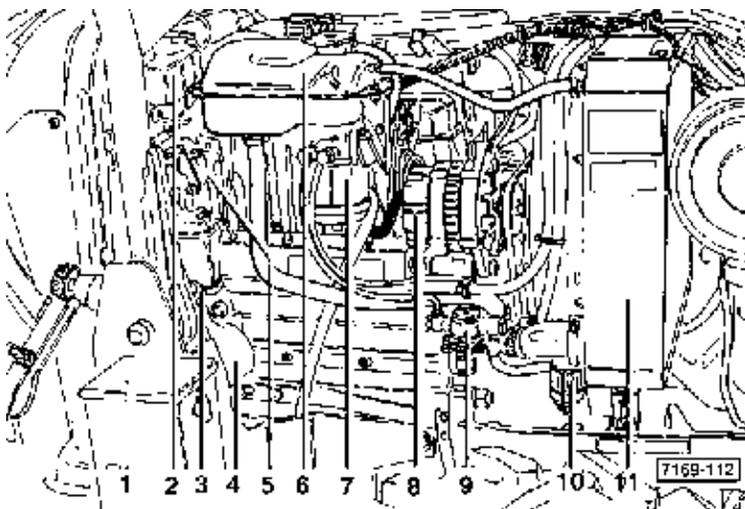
Côté droit moteur - (3 cylindres)
